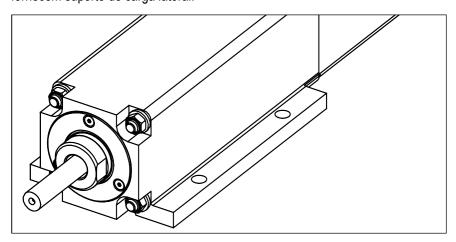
O projeto do GSWA33 Guided inclui este conjunto que tem estas funções: dispositivo anti-rotação, dispositivo de montagem, suporte de carga lateral.
